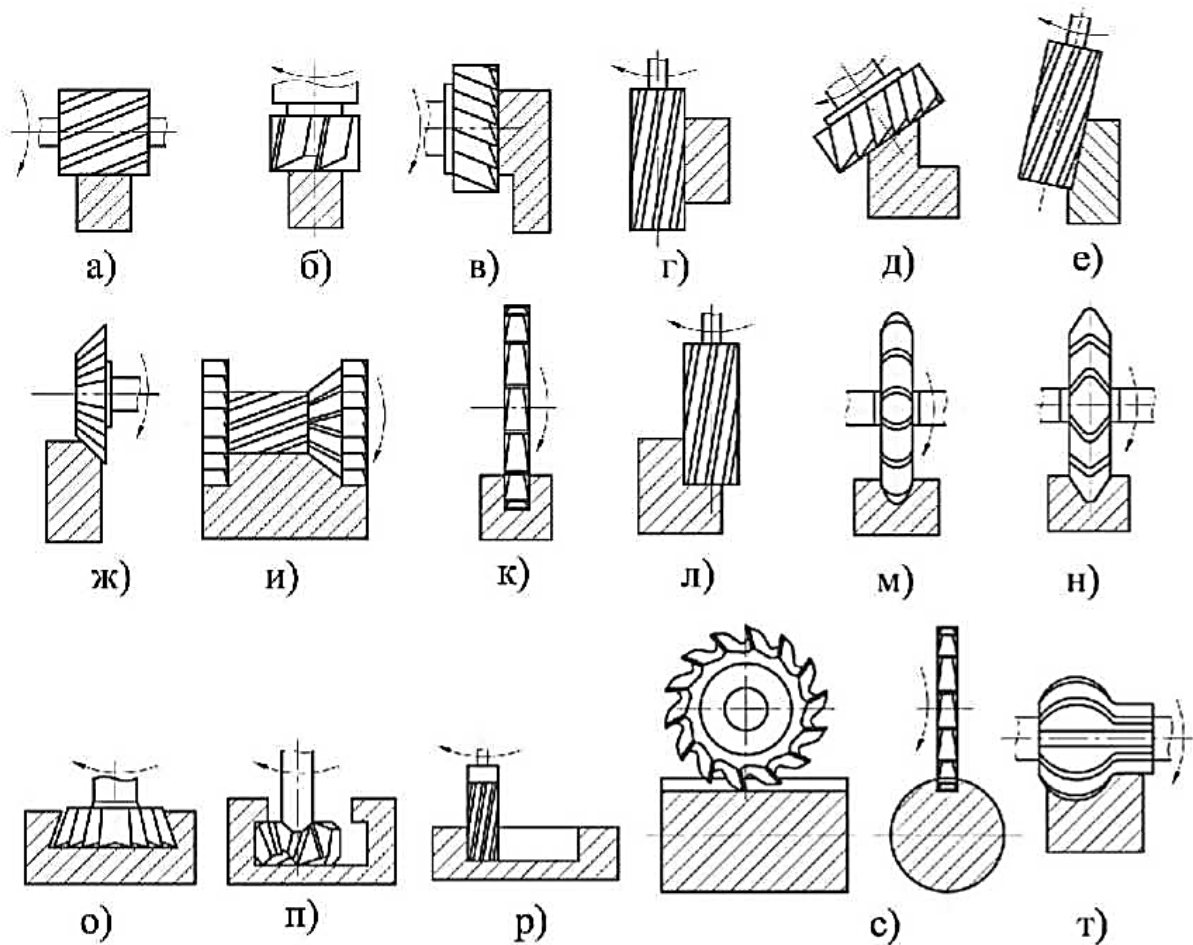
Схеми оброблення поверхонь на фрезерних верстатах
